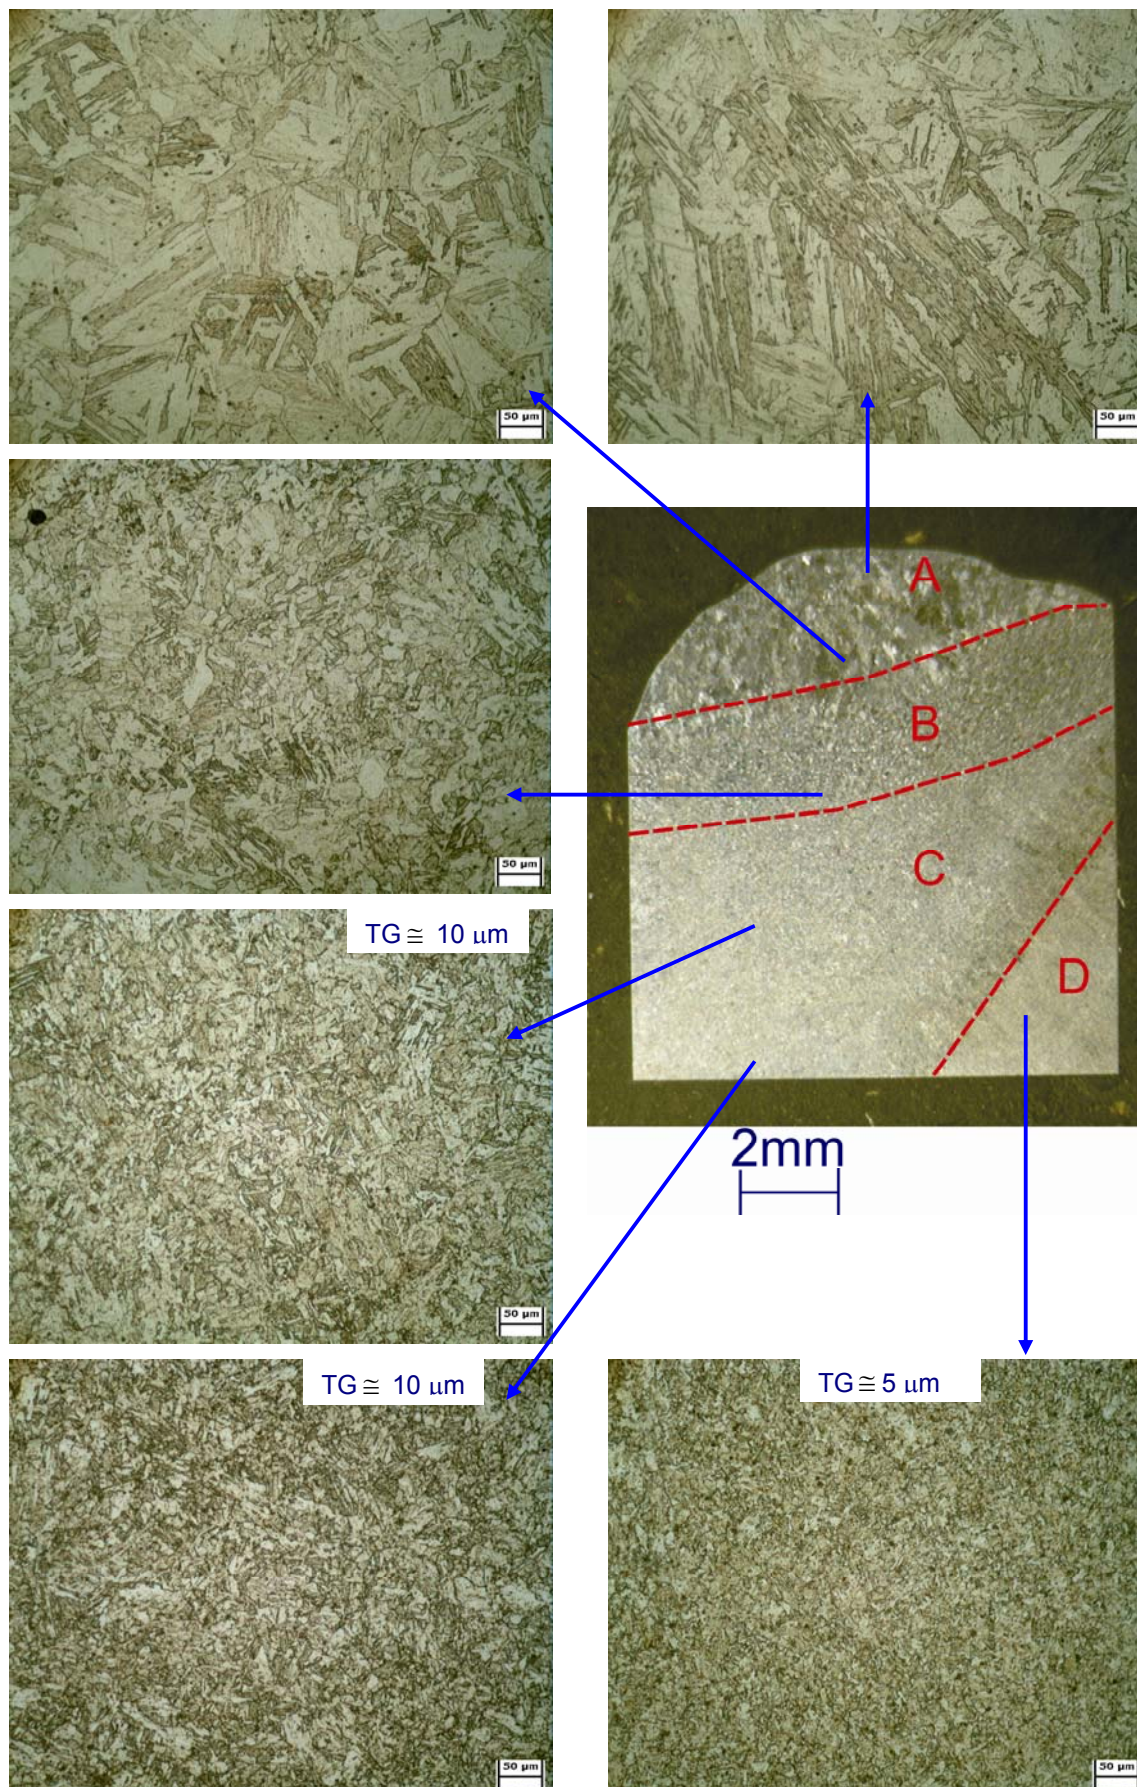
Passe TIG energia de soldagem 0,93 KJ/mm.
